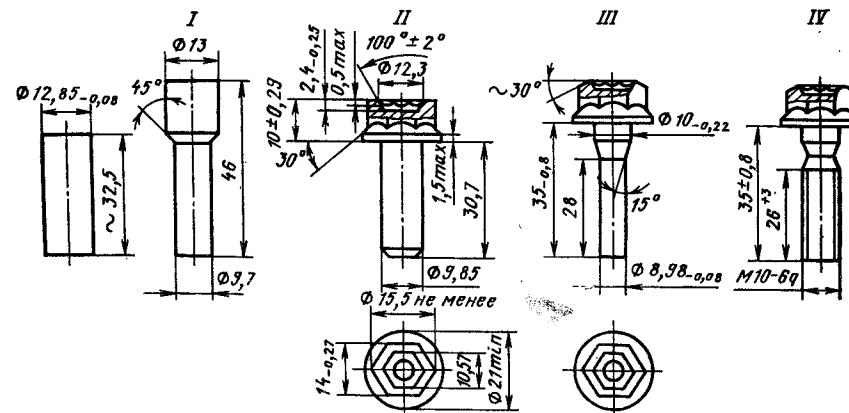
Технологический процесс штамповки и накатки резьбы при изготовлении болтов М10—6g×85 с фланцем на автоматической линии Л120
